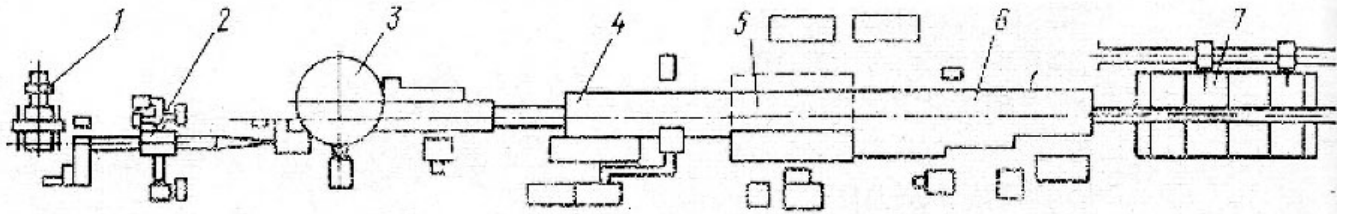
Схема расположения оборудования ТЭСА 6—30 фирмы «Weap—Damiron» (Франция) для сварки труб выпрямленным током:
